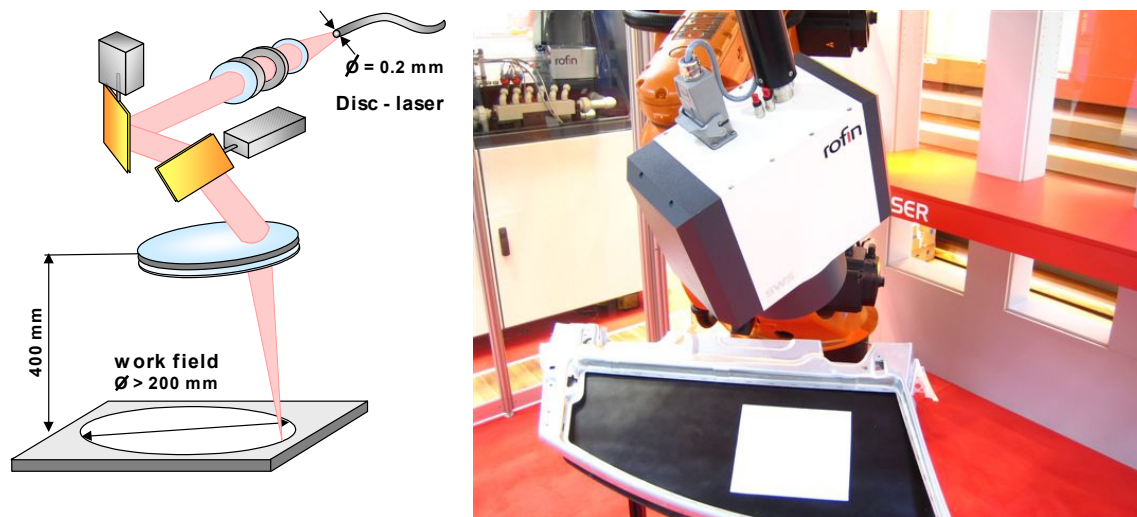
Scanner-Schweißen mit Scheibenlaser
